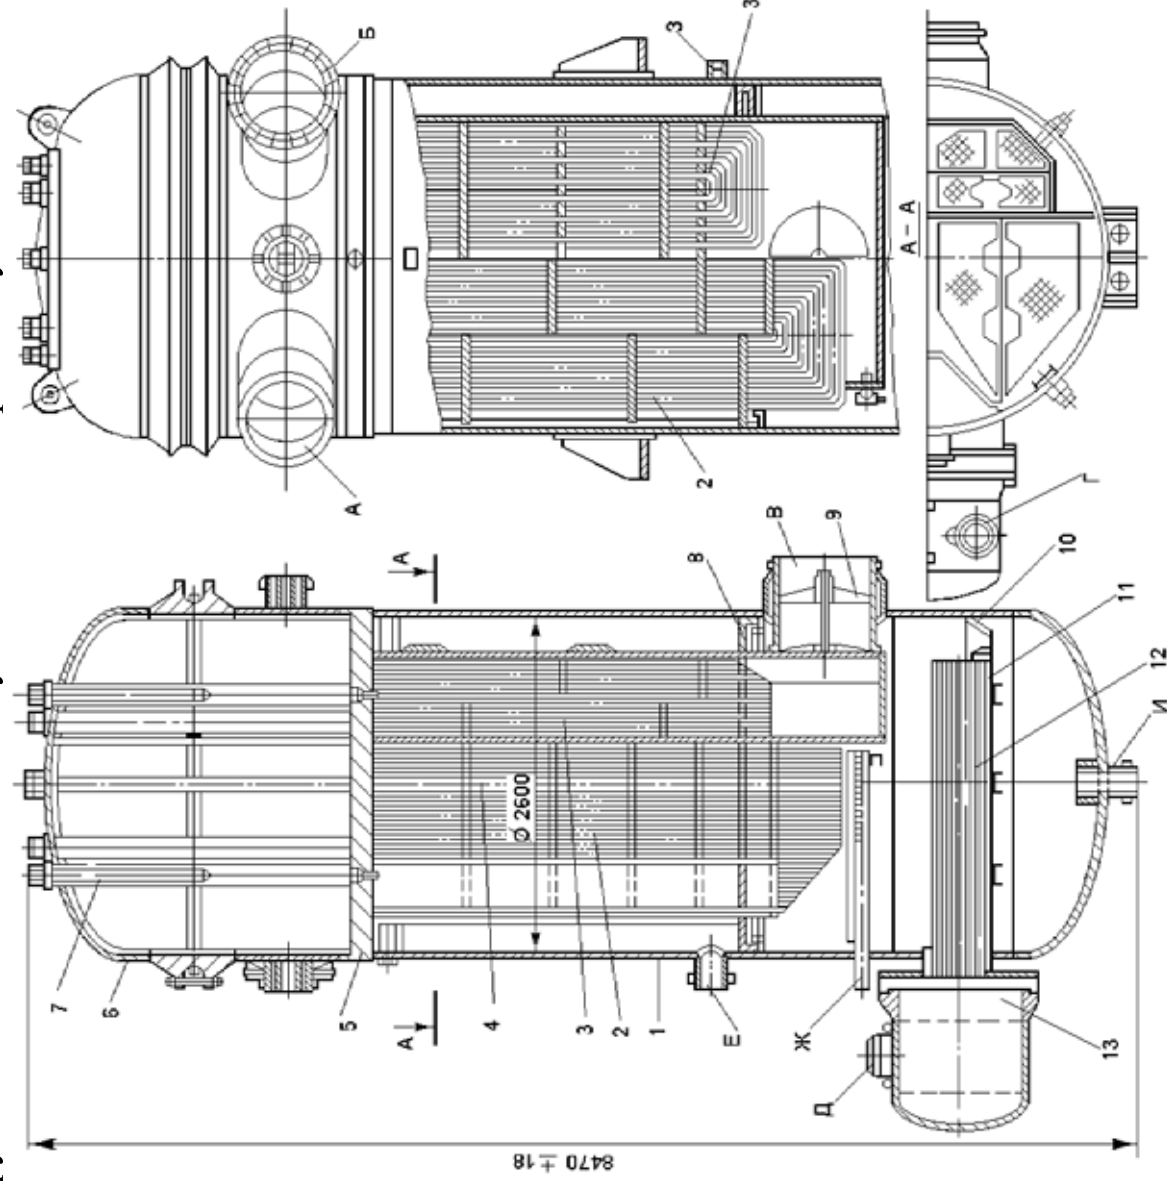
Подогреватель низкого давления ПН-1900-32-7-1 энергоблока К-800-240 ЛМЗ:
